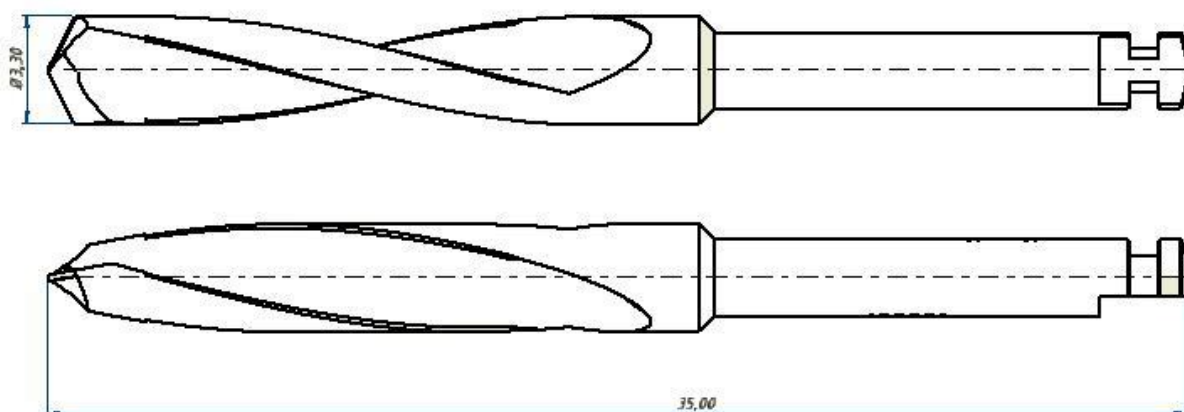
Desenho ilustrativo das dimensões das brocas: 3,3 x 35 mm
